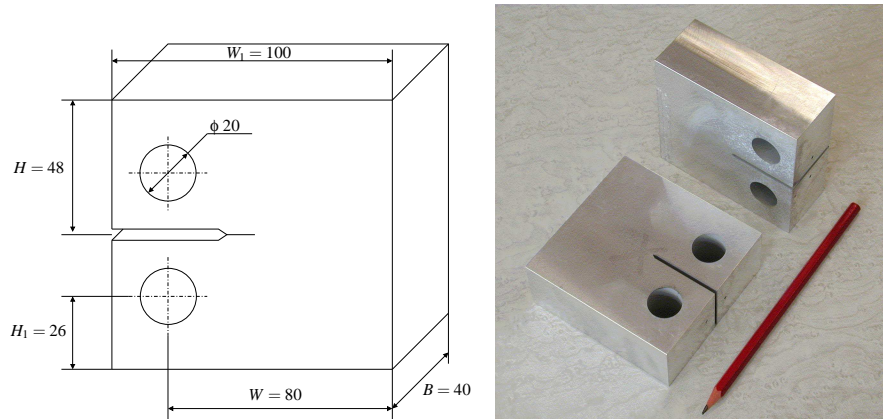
Géométrie en mm de l'éprouvette CT B40W80
